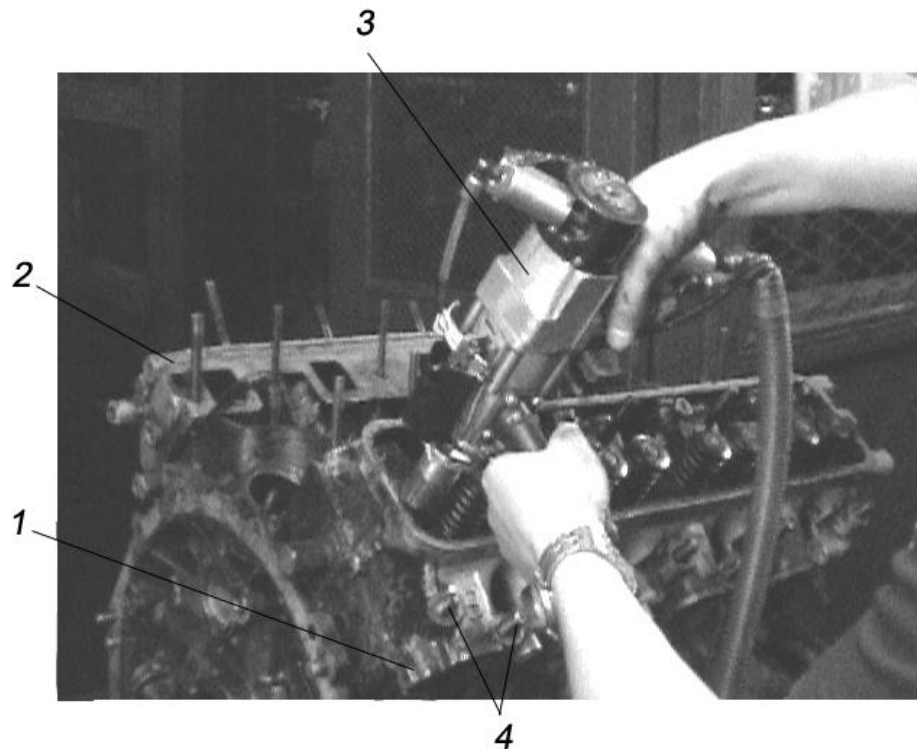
Складання різьбових з'єднань кріплення головок блока двигуна ЗМЗ-53: 1,2 ліва і права головки блока; 3 – адаптивний гайкокрут; 4 – шпильки М11×1 кріплення головки блока.
